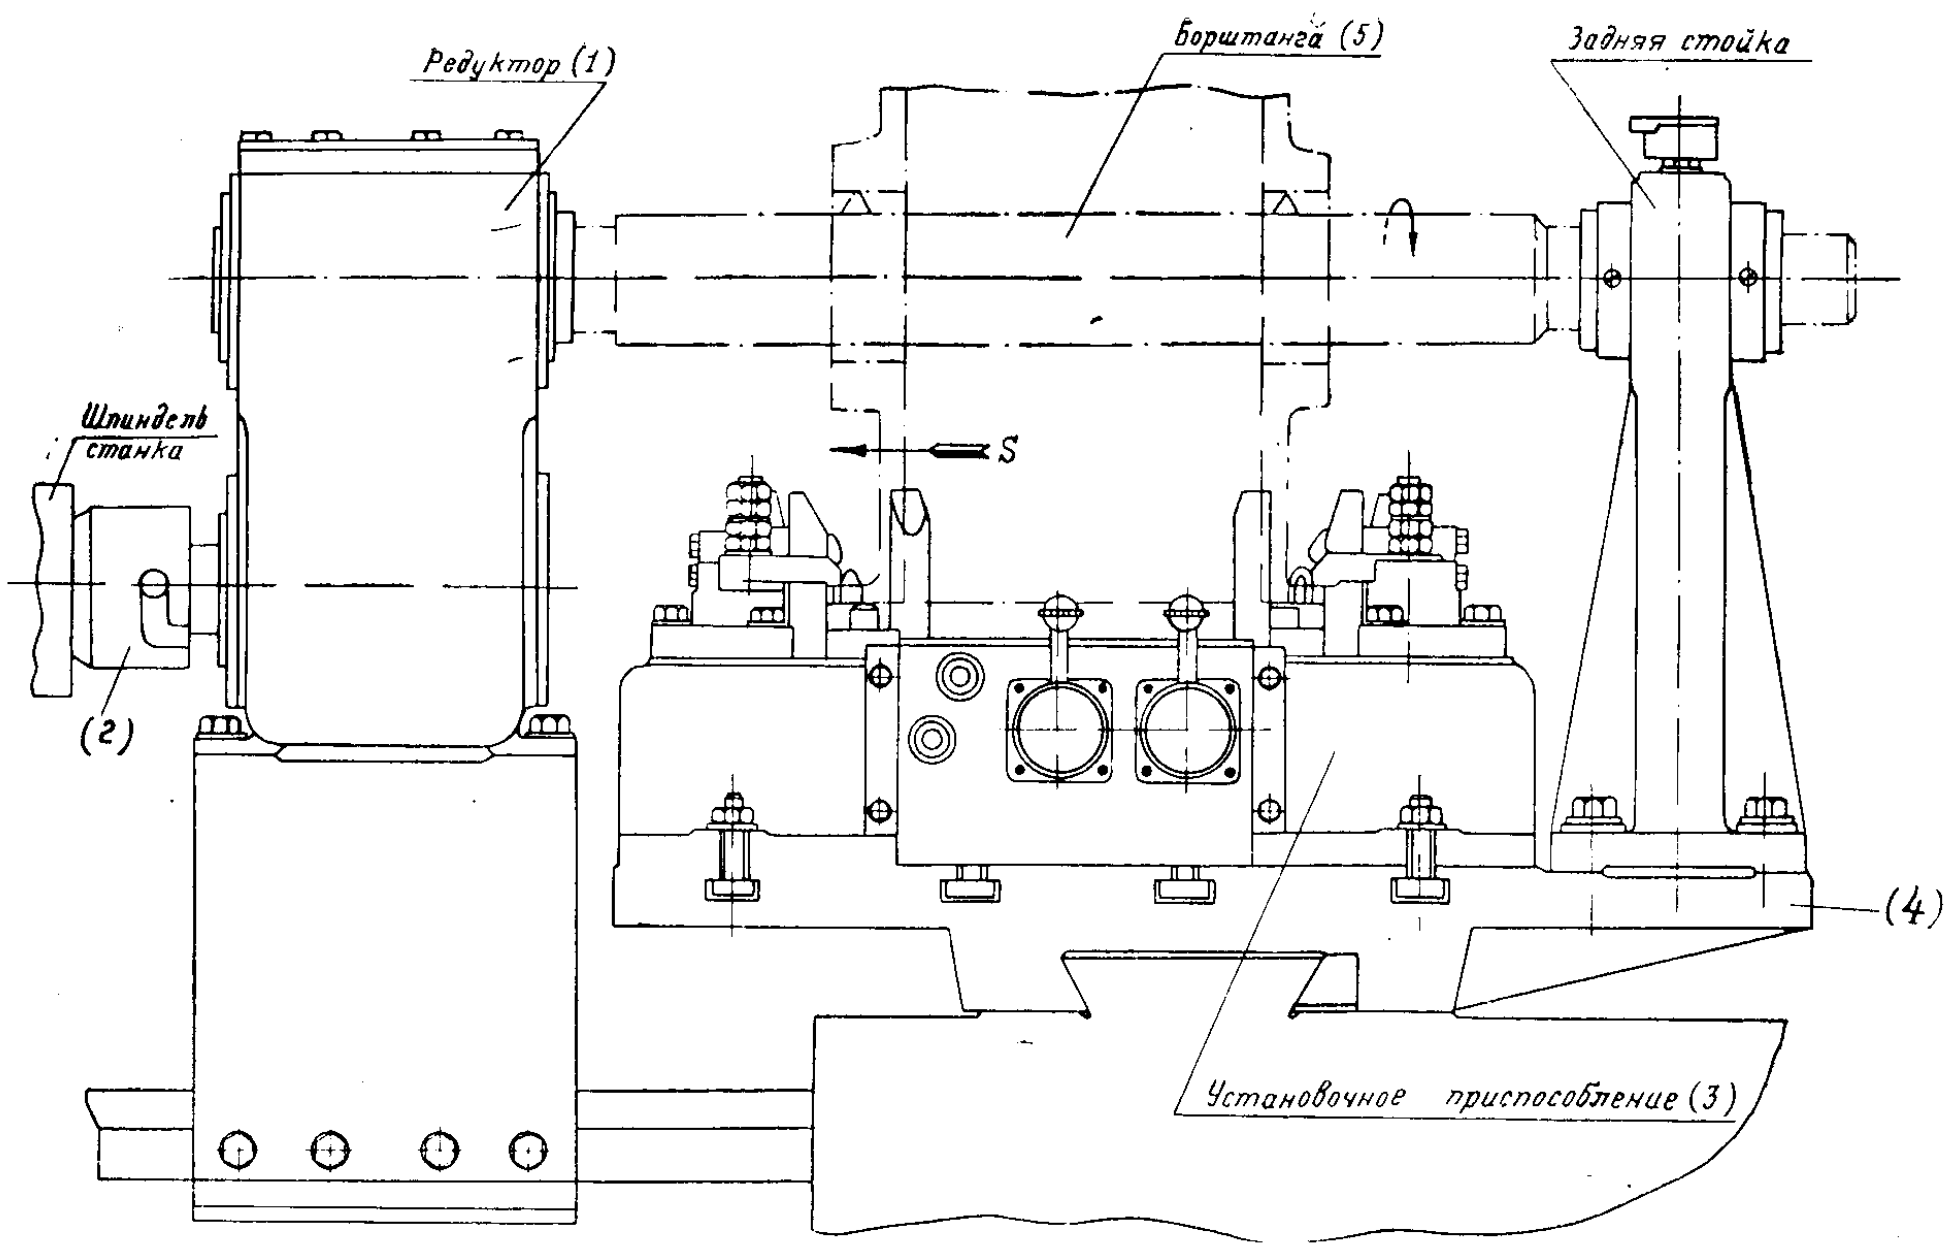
Групповая агрегатная установка для расточки корпусов редукторов.
